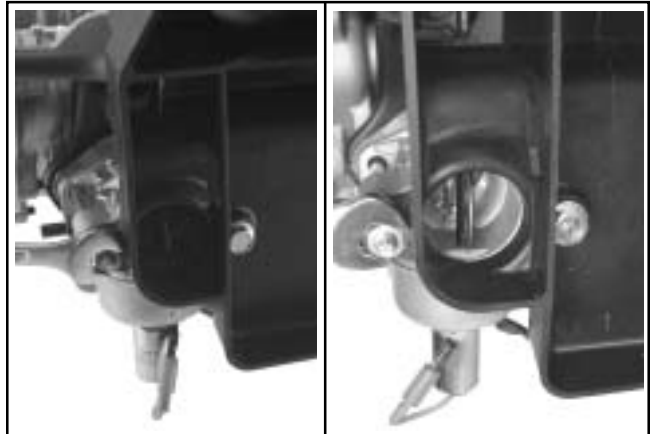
Desmontaje de los tornillos del soporte del filtro de aire.
